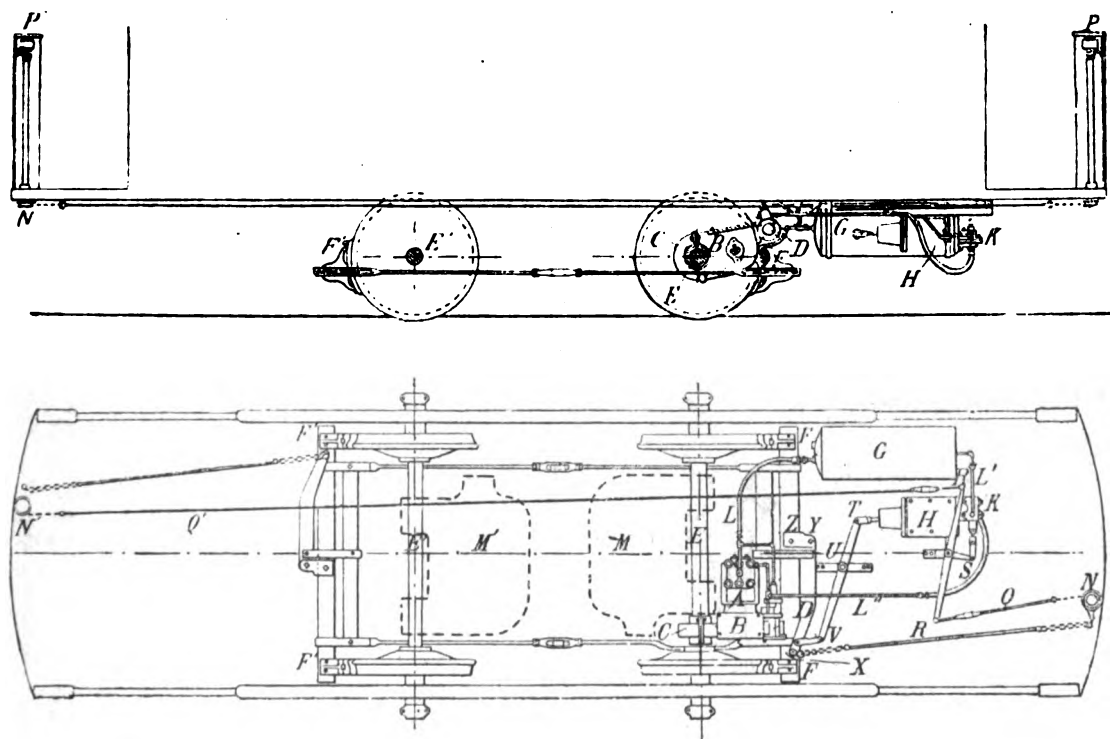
et 2. — Frein à air comprimé de la Standard Air Brake Company.
